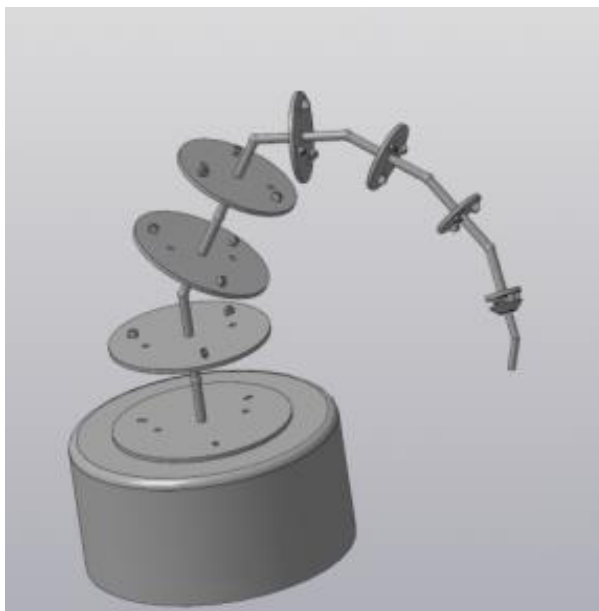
Сварочный робот на базе гибкого манипулятора
